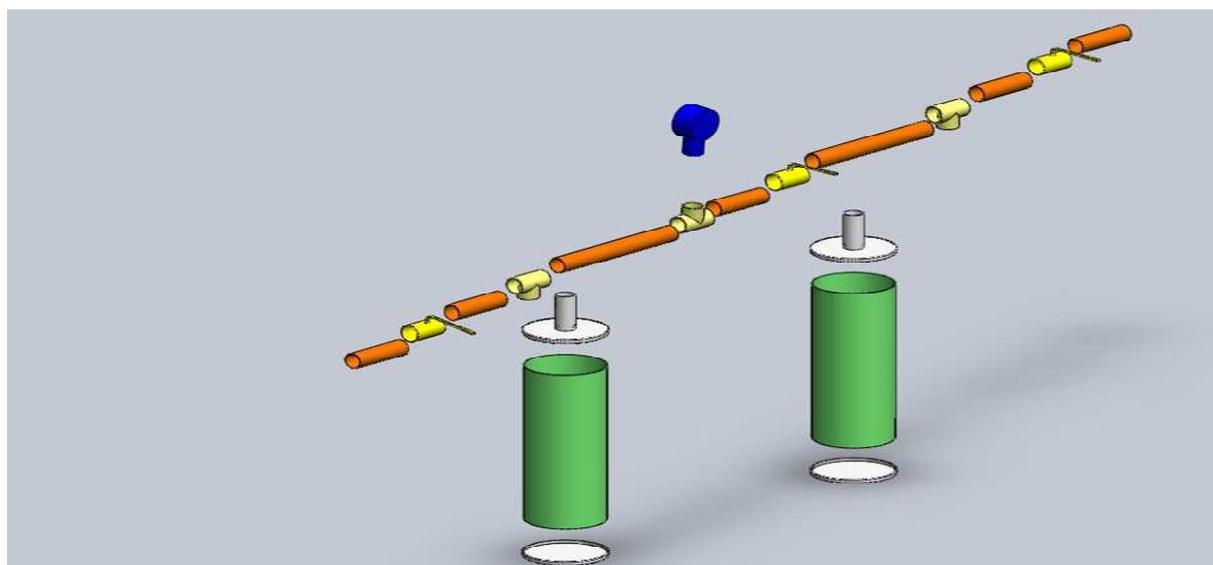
Desenho explodido de protótipo de picnômetro a ar.
